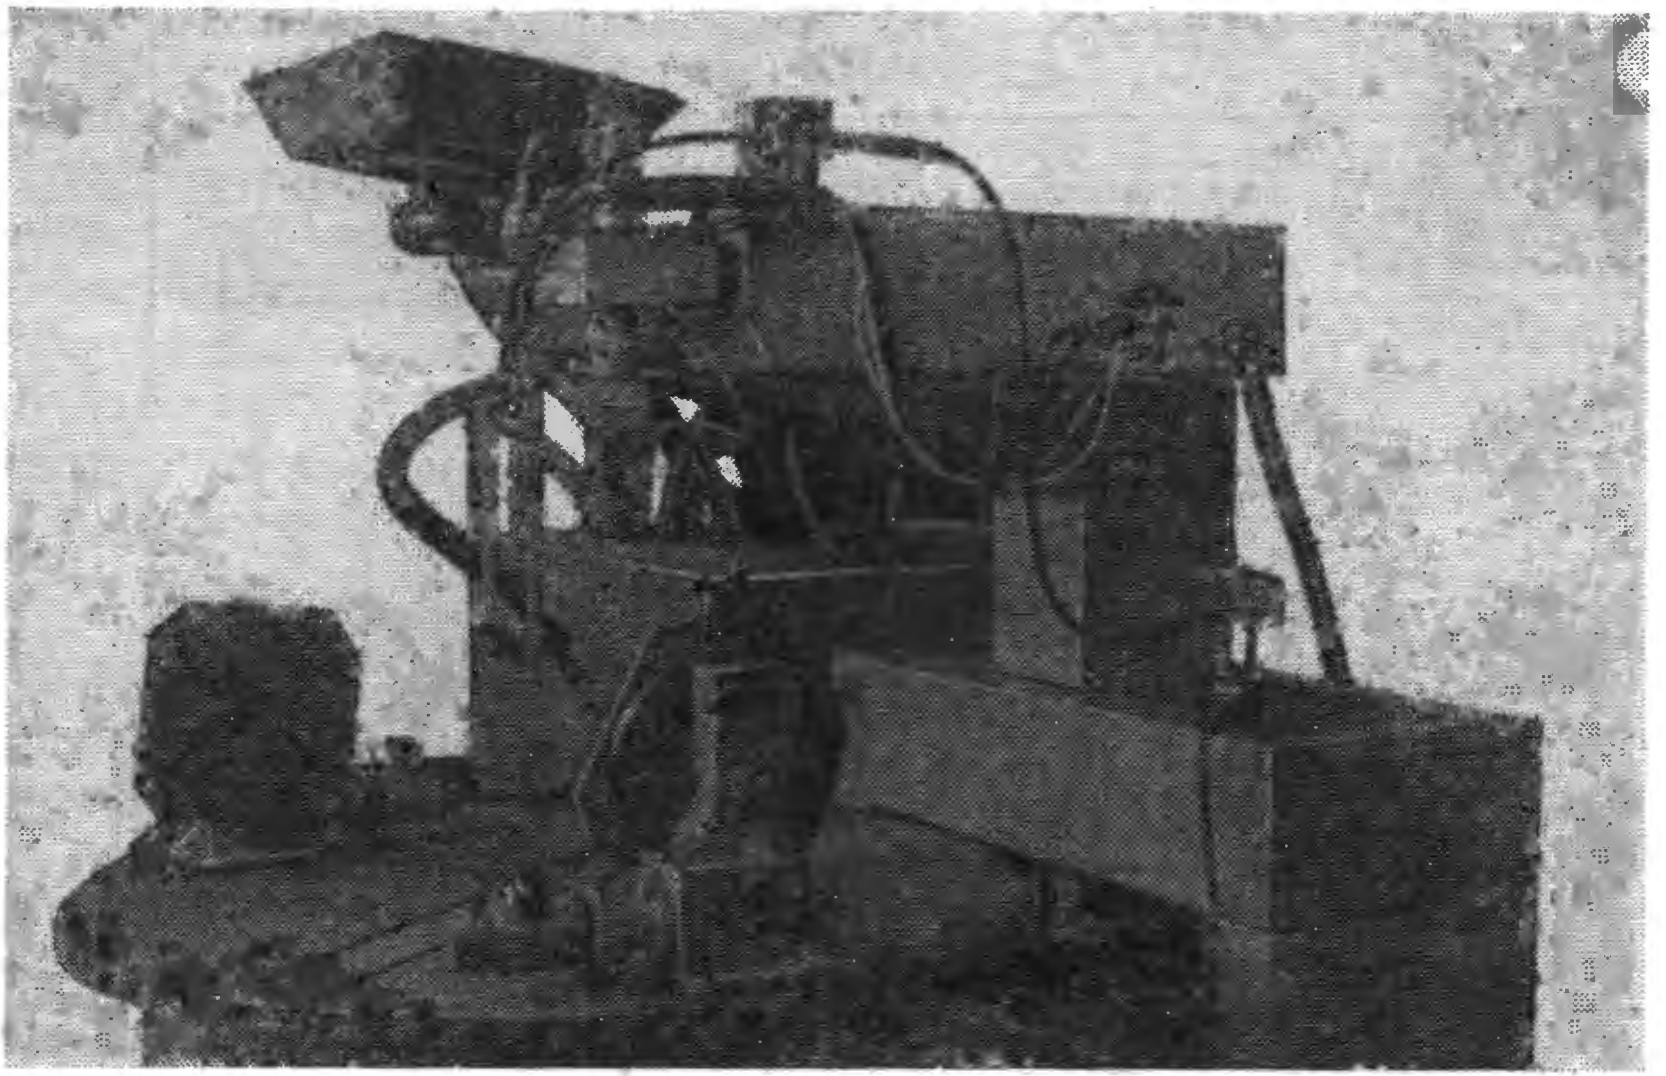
Станок УД327 с ЧПУ для дуговой сварки швов сложной формы
